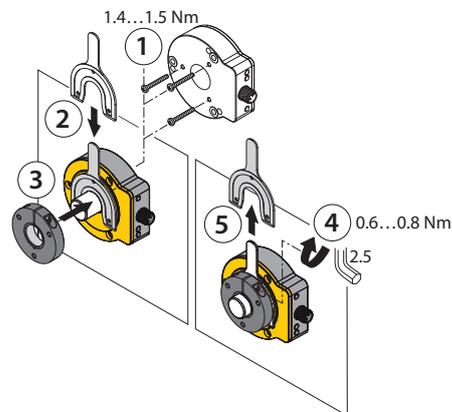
Rückseitig montieren – Wellendurchmesser bis 20 mm
